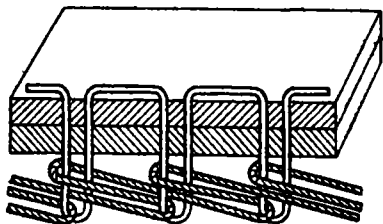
Сквозная строчка линейная цепного двухстрочного стежка
